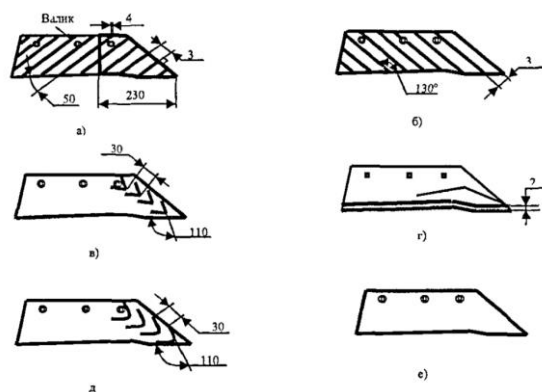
Схема зміцнення поверхні леміша шляхом наплавлення одиночними валиками
